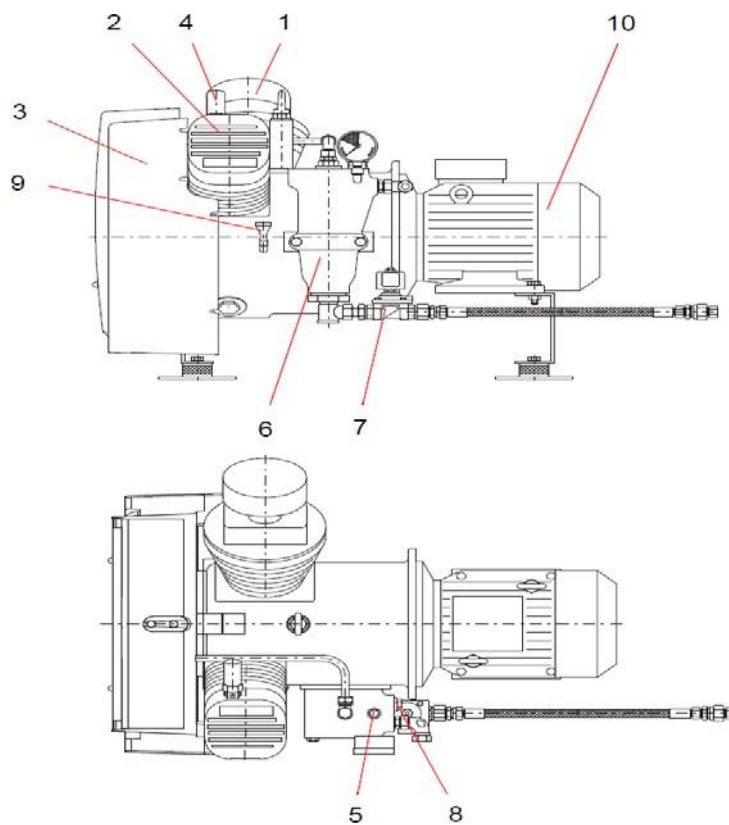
Компресор WP 22L: 1 - циліндр першої ступені; 2 - циліндр другої ступені; 3 - охолоджувач; 4 - запобіжний клапан першої ступені; 5 - запобіжний клапан другої ступені; 6 - конденсатний сепаратор; 7 - дренажний клапан; 8 - плавкий запобіжник; 9 - масляний щуп; 10 – електродвигун
